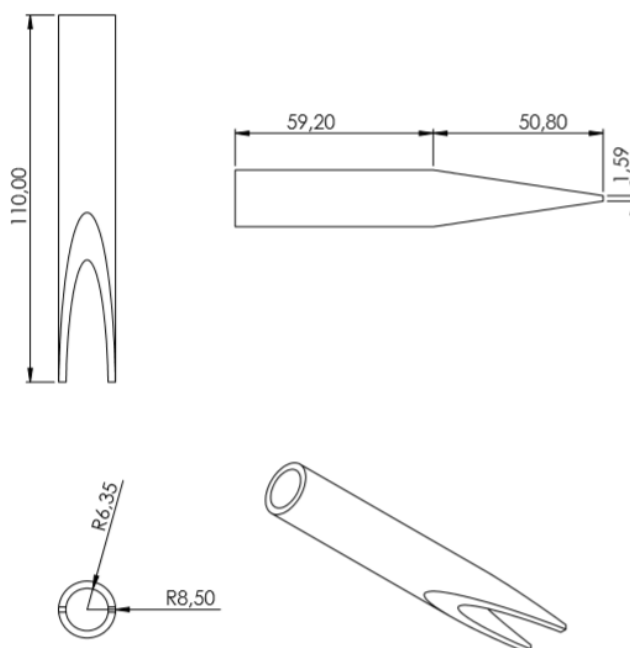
Dimensiones para la fabricación del elemento 1 de la boquilla
